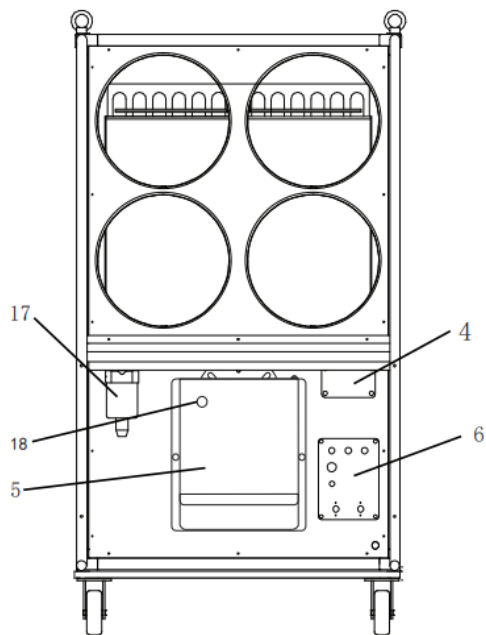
Внешний вид устройства IY135W/IY220W и его компоненты
